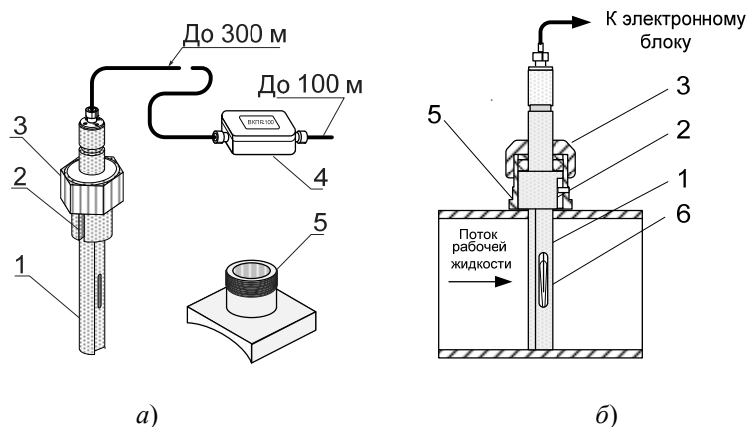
Погружной вихревой расходомер (а), установленный на рабочем трубопроводе (б):
